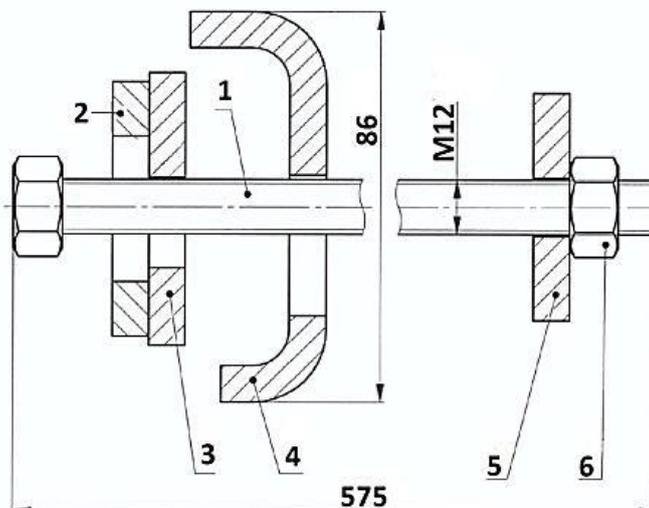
Болт из набора «СНКЛ-4» со всеми дополнительными деталями: 1 – болт; 2 – накладка; 3 – пластина; 4 – швеллер; 5 – шайба; 6 – гайка М12.
